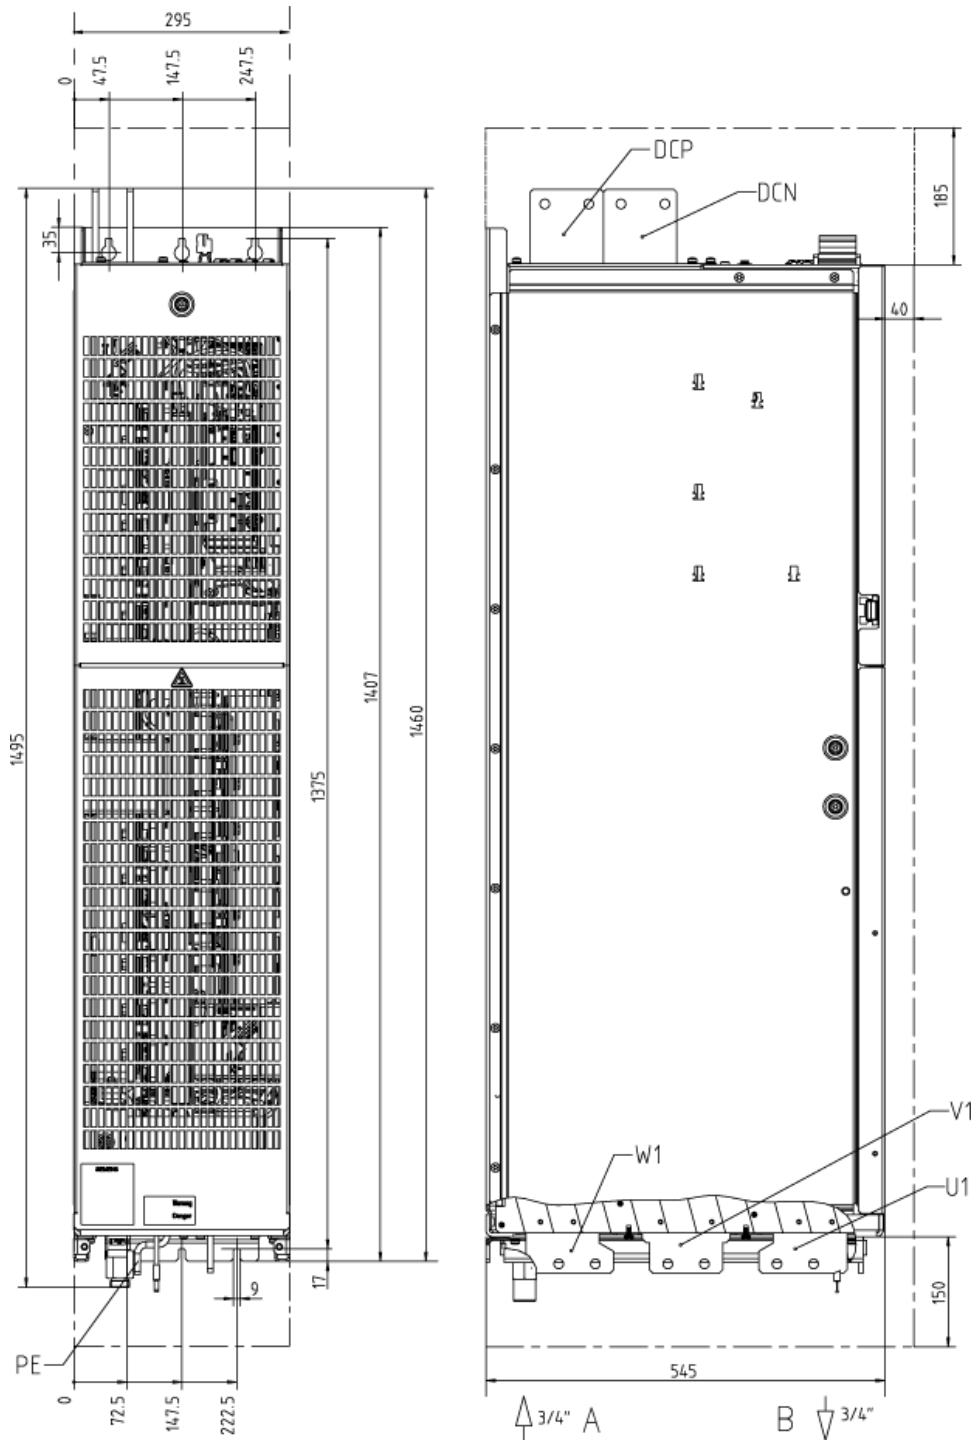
Габаритный чертеж активного модуля питания, типоразмер JXL, каталожный номер 6SL3335-7TE41-0AA3, 6SL3335-7TE41-4AA3, 6SL3335-7TG41-0AA3, 6SL3335-7TG41-3AA3. Вид спереди, вид сбоку
